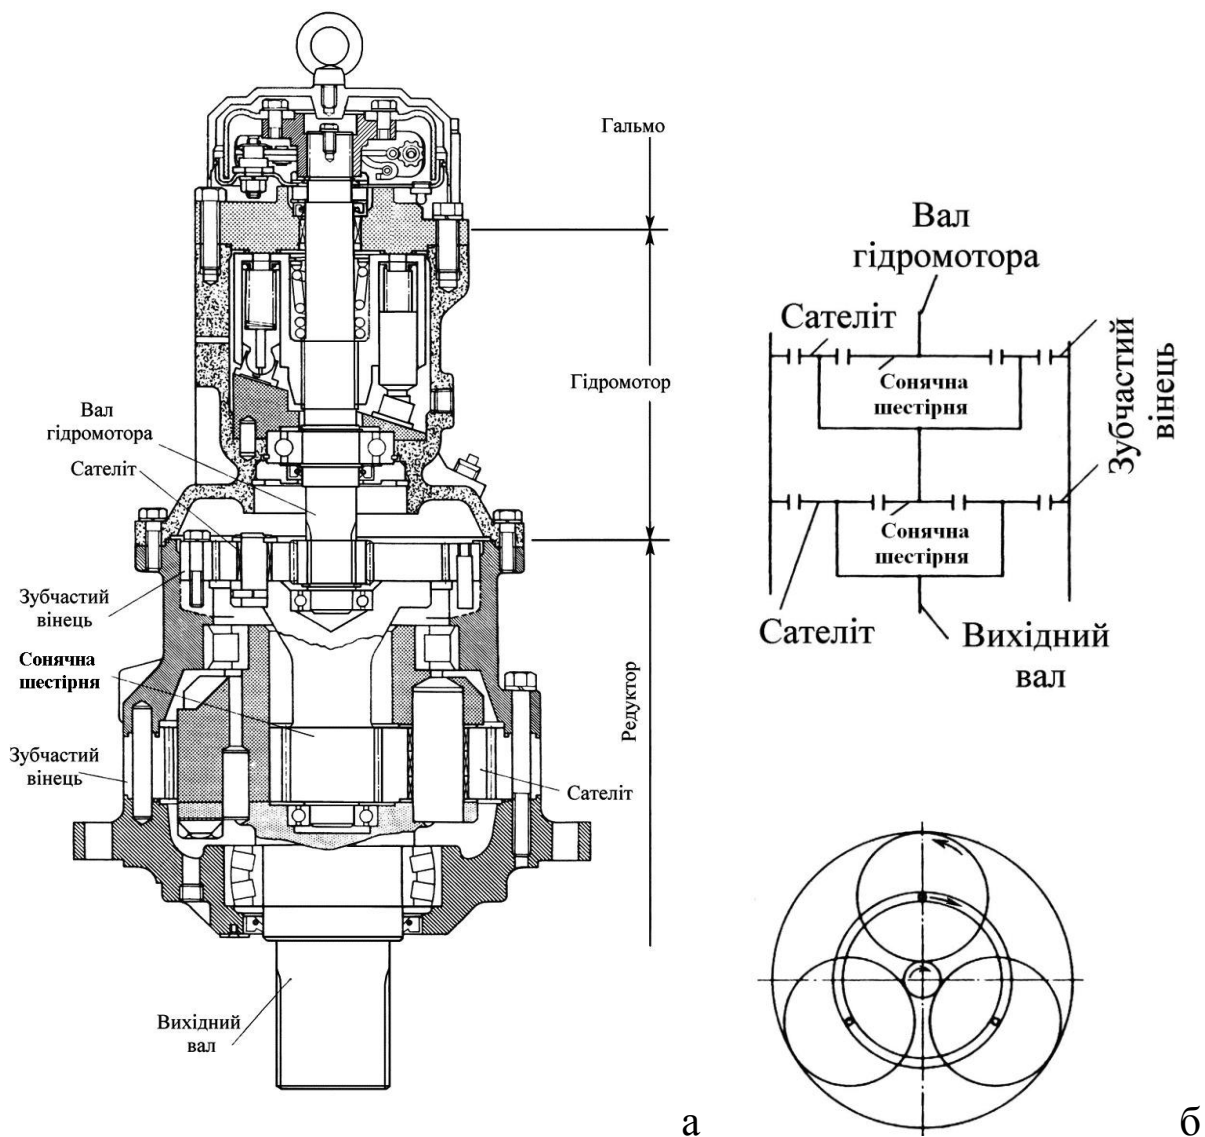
Механізм обертального руху платформи крана TADANO: а – переріз механізму; б – схемне рішення планетарного редуктора
